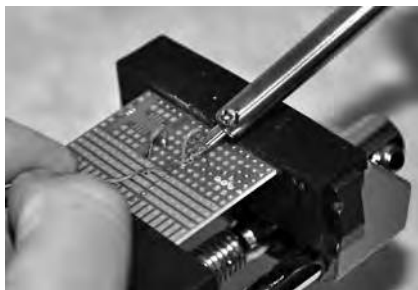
Il saldatore e lo stagno devono essere posati esattamente sulla piazzola di saldatura. La saldatura dovrebbe durare solo pochi secondi..
